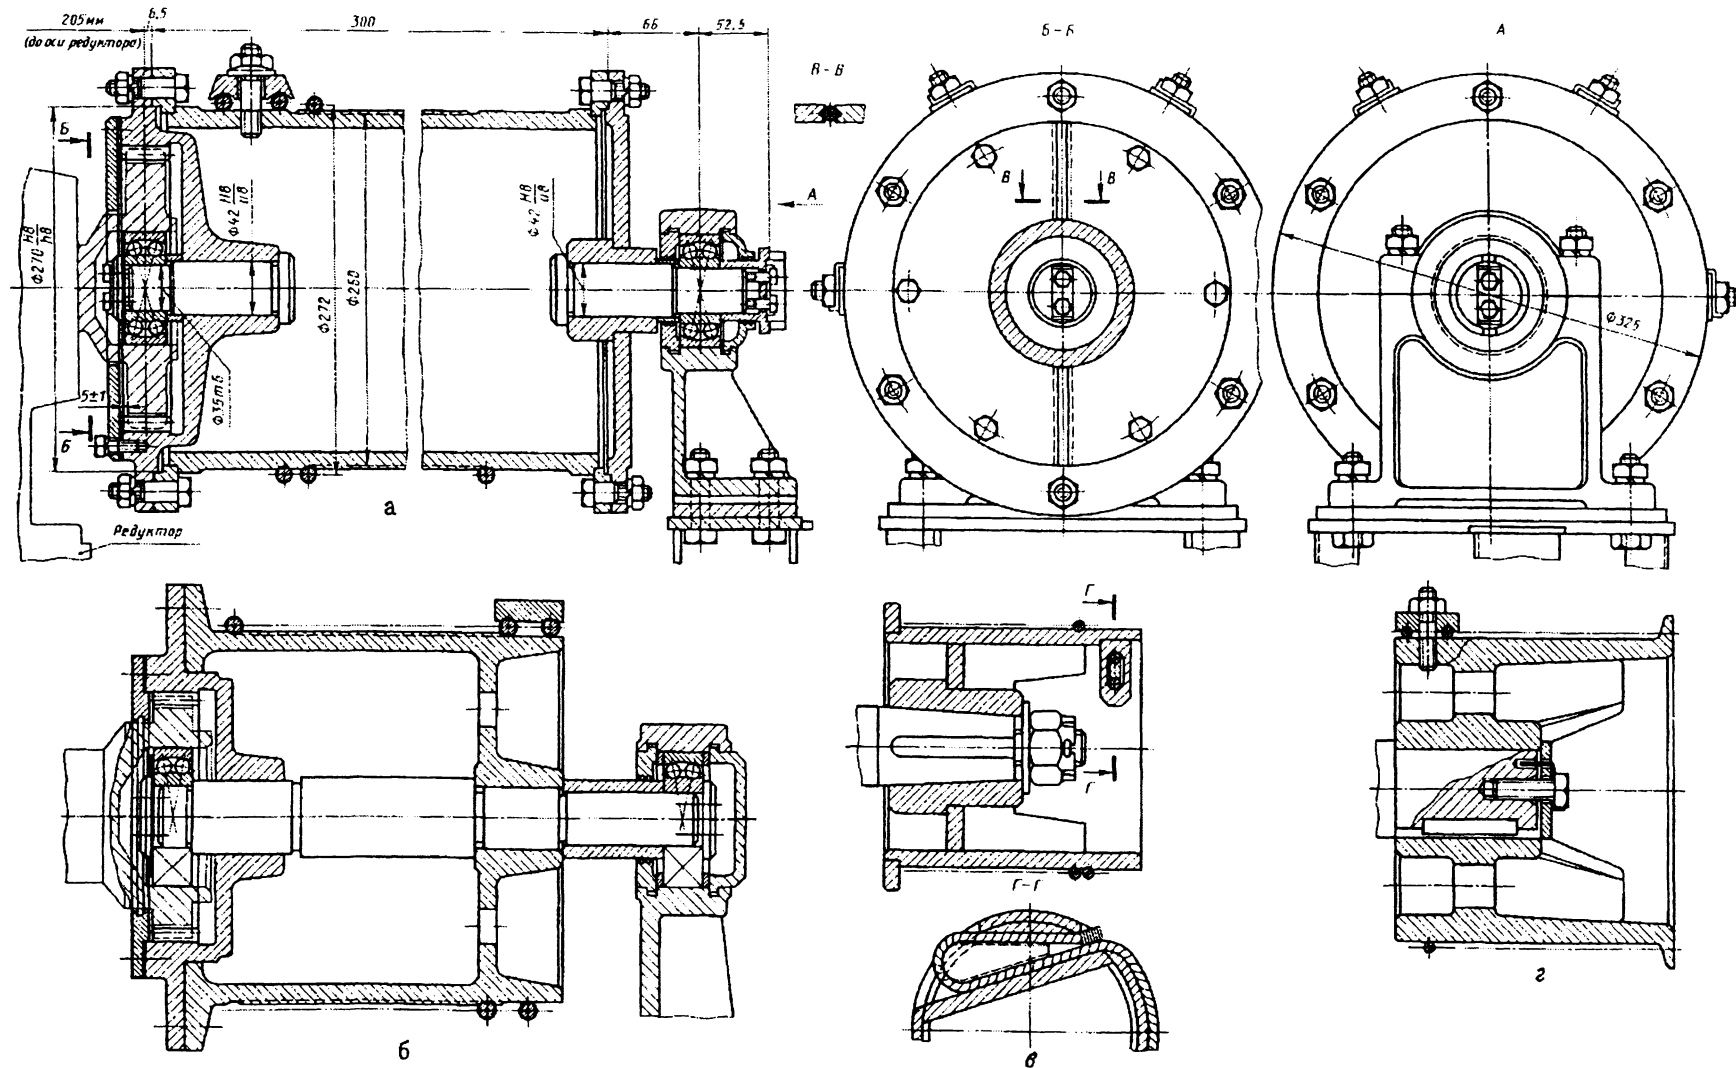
Примеры конструкций установки барабана механизма подъема груза [4]:
